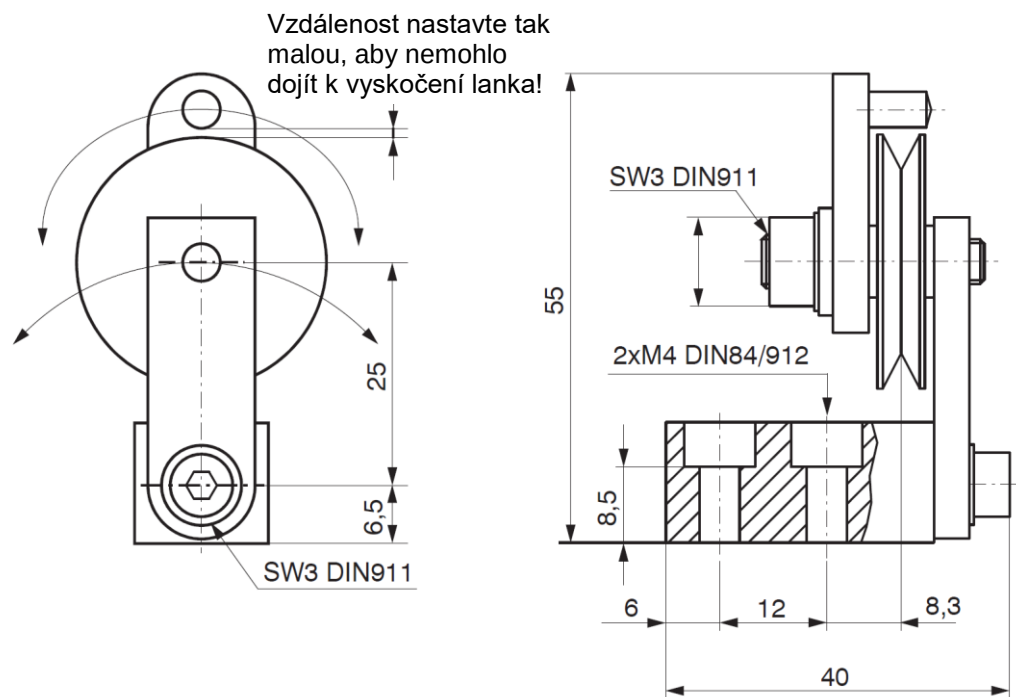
Magnetický držák MH2-WDS, rozměry jsou uvedeny v mm.
